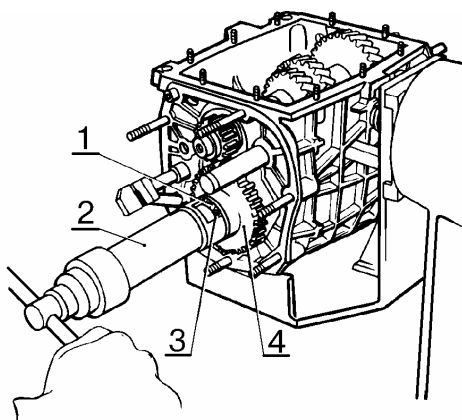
Снятие стопорного кольца ведомой шестерни заднего хода с вторичного вала:
